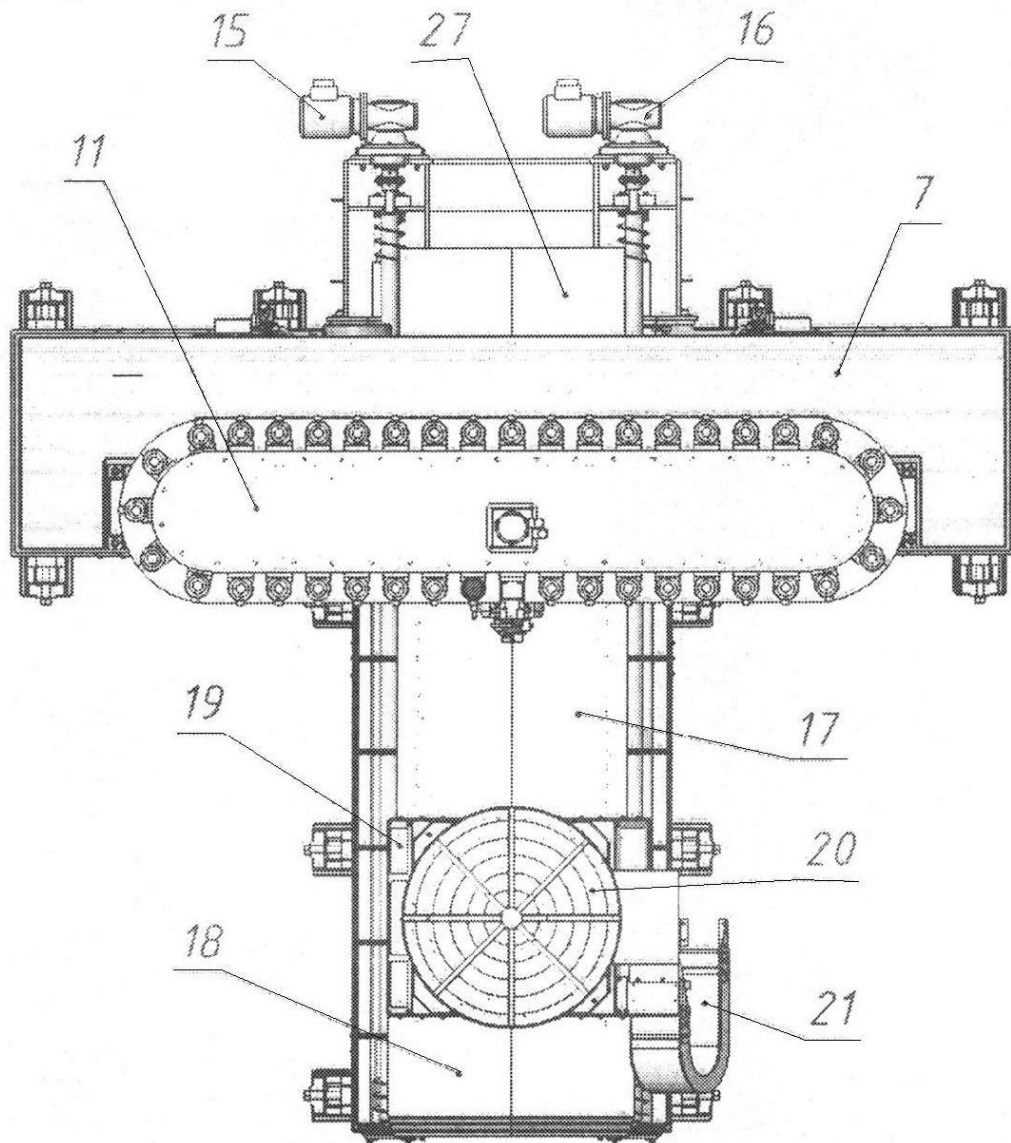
Високошвидкісний обробний центр типу «біпод» з гібридною кінематичною структурою (вигляд зверху)
